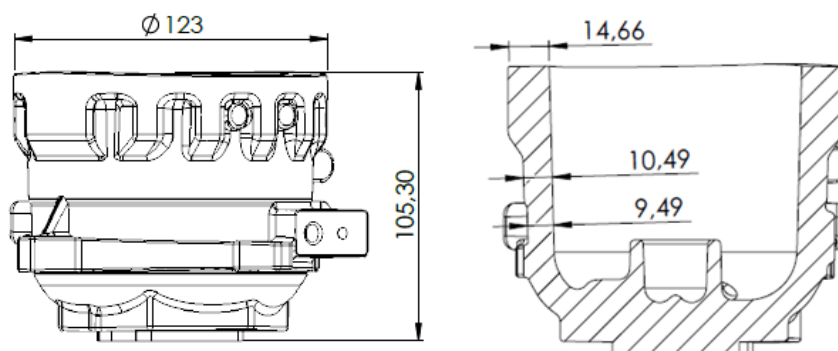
Esquema de dimensões gerais (em mm) da peça obtida por Rheocasting designada por MotorHousing R006
